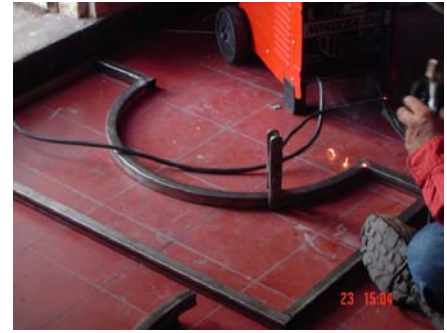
Acoplamiento de los tubos. Soldadura.
